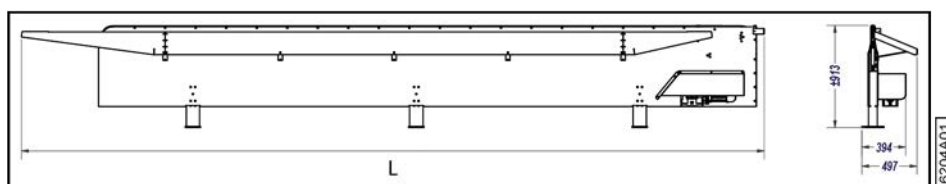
Dimensions de la machine avec tôle de redressement côté tête
